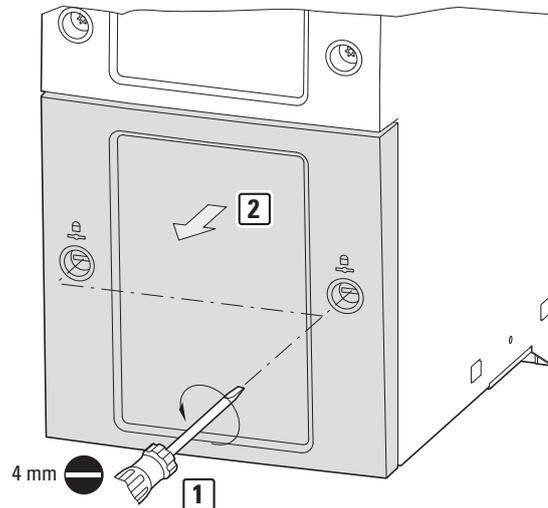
Entfernen des Gehäusedeckels in Baugröße FS4 oder FS5
